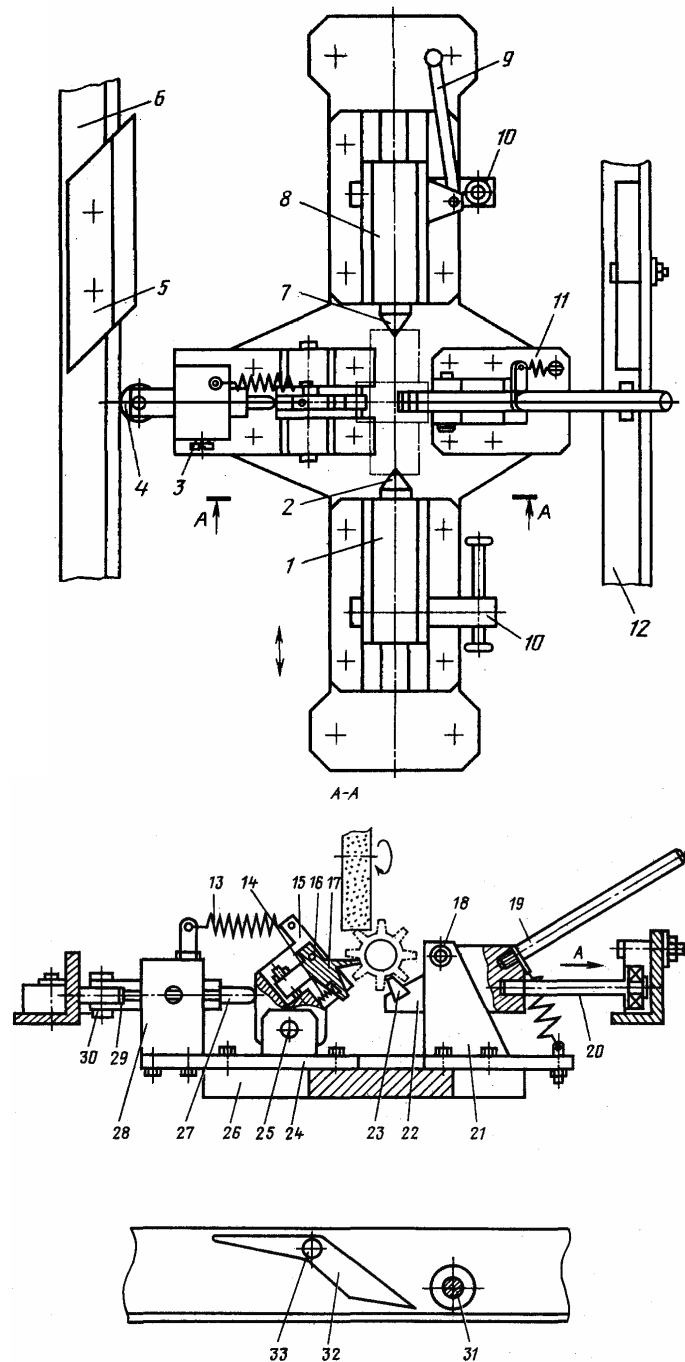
Напівавтоматичне пристосування для шліфування бокової поверхні зубців шестерень:
